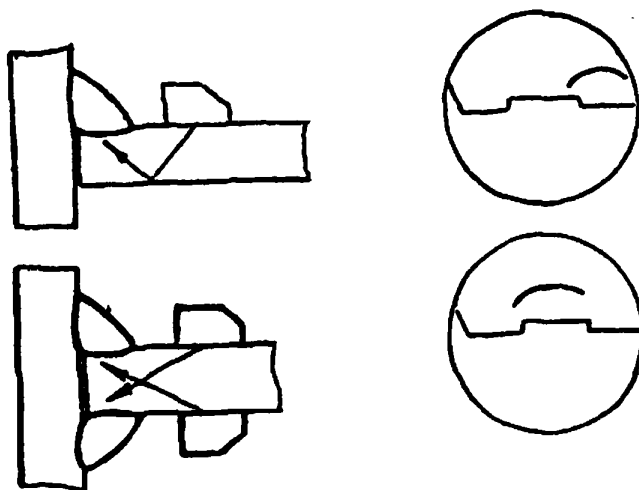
Схемы контроля тавровых сварных соединений, выполненных без разделки кромок;
